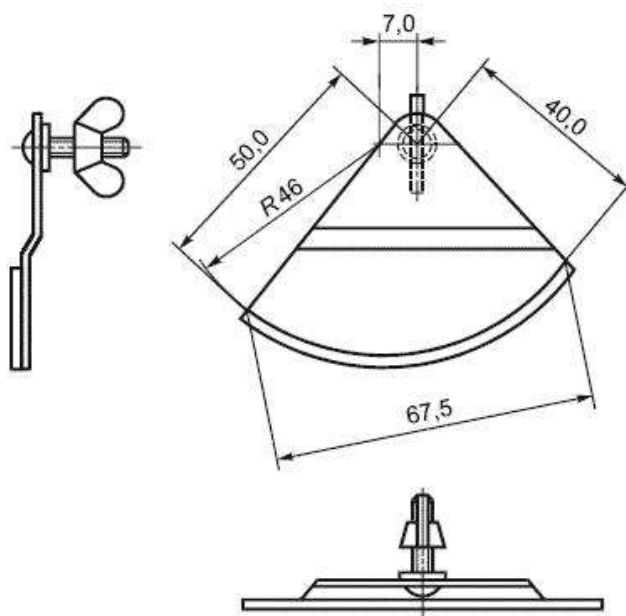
Пластинка фиксатор подвижного стержня с конусом
